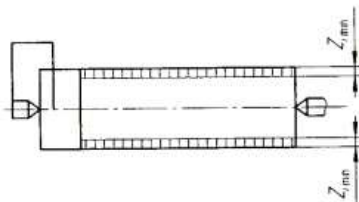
Ескіз обробки заготовки, закріпленої в центрах
